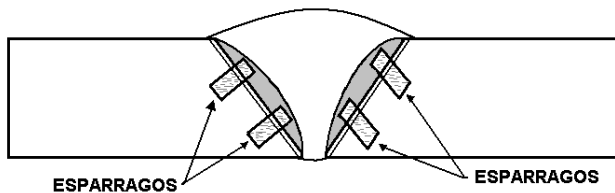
Soldadura en fundición con espárragos insertos. [10].
